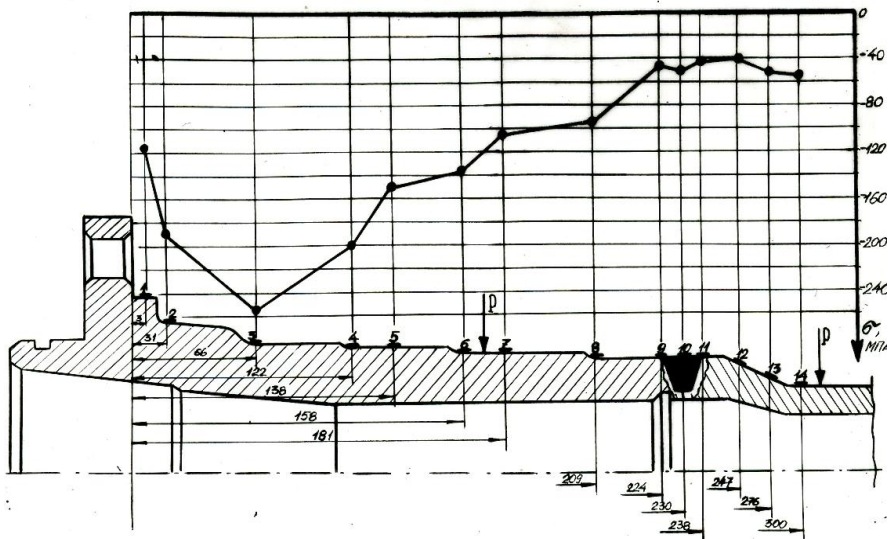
Схема размещения тензорезисторов и распределение напряжений в цапфе сварной конструкции из стали 18Х2Н4МА (при испытаниях на изгиб)
